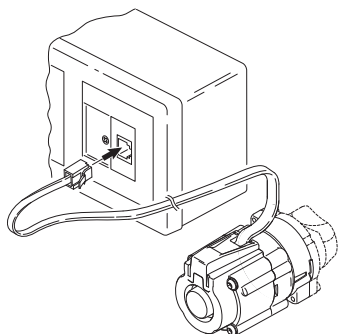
Pumpenkabel am Modul Heatfixx aufstecken
